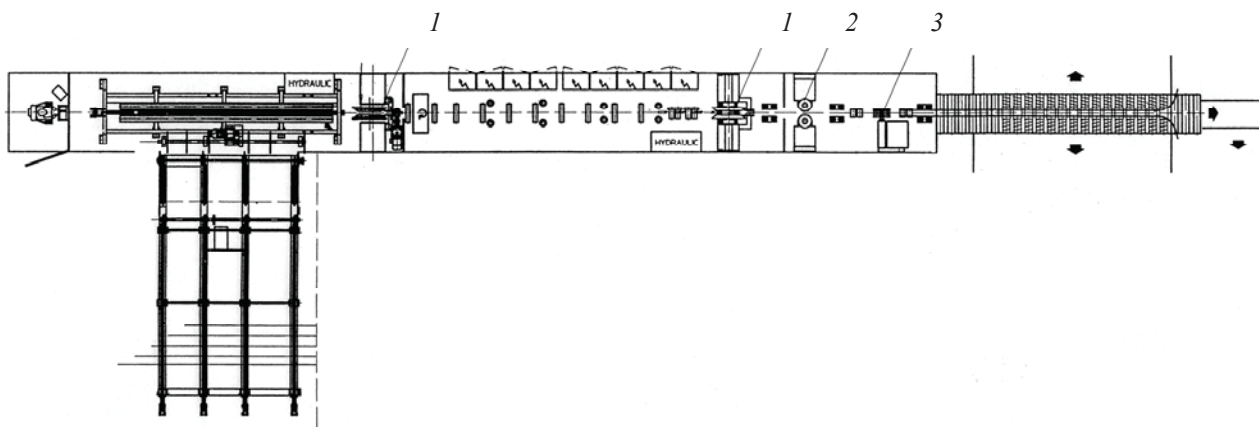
Общий вид фрезерно-профилирующе-пильного комплекса GIGA 02 В фирмы А.СOСТА (Италия):
